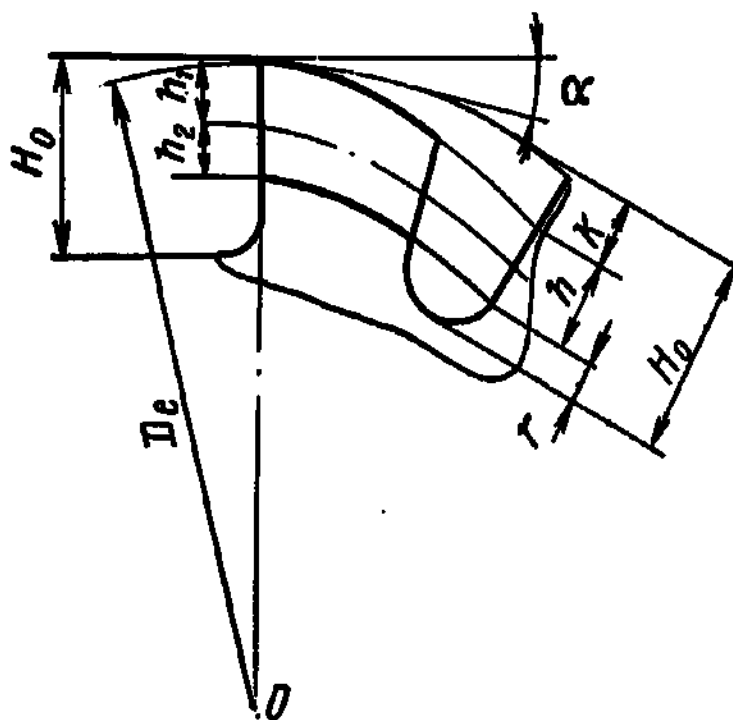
Конструктивные параметры зуба червячной модульной фрезы
